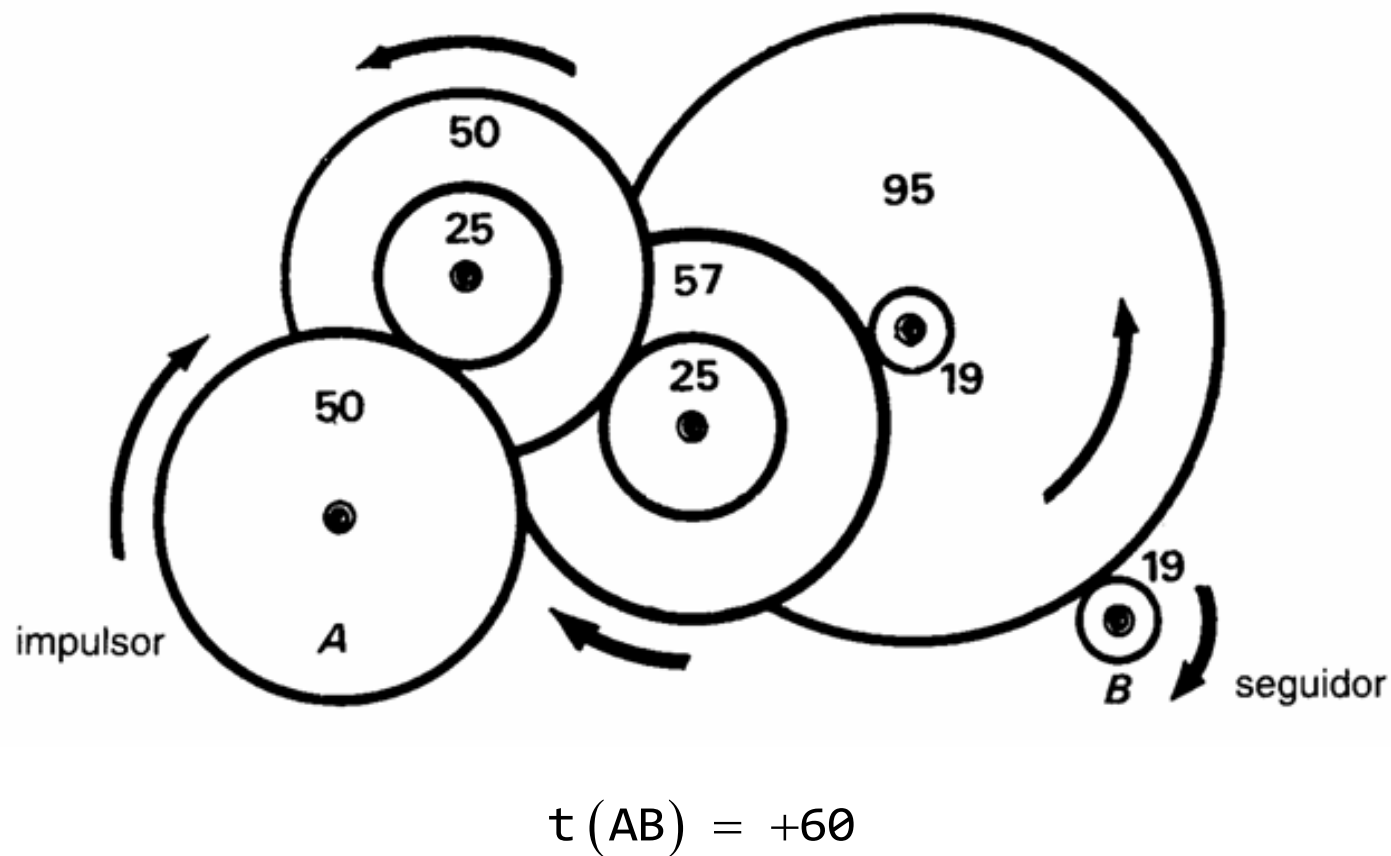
Tren de Engranajes Compuesto en un Reloj Tradicional.
